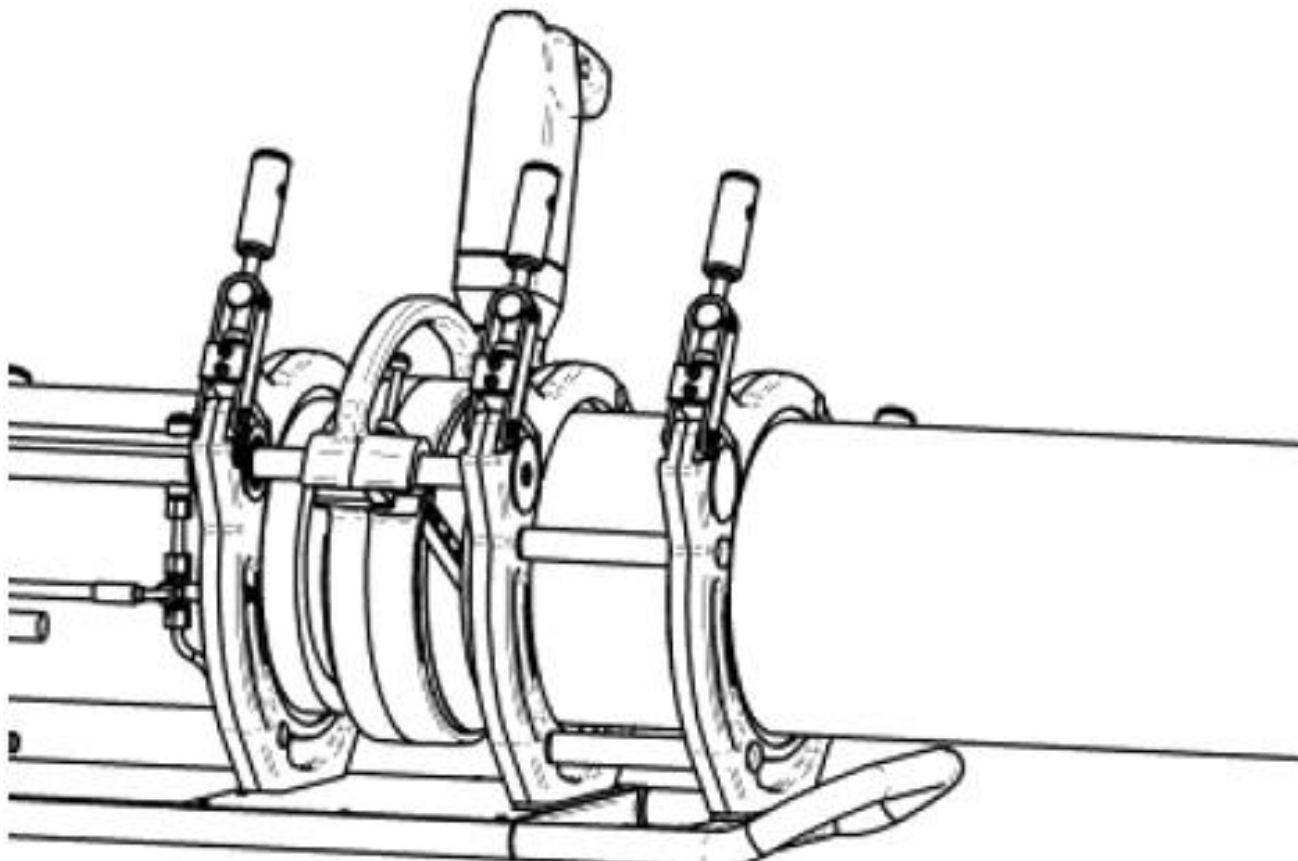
Установка торцевателя между свариваемыми торцами труб
